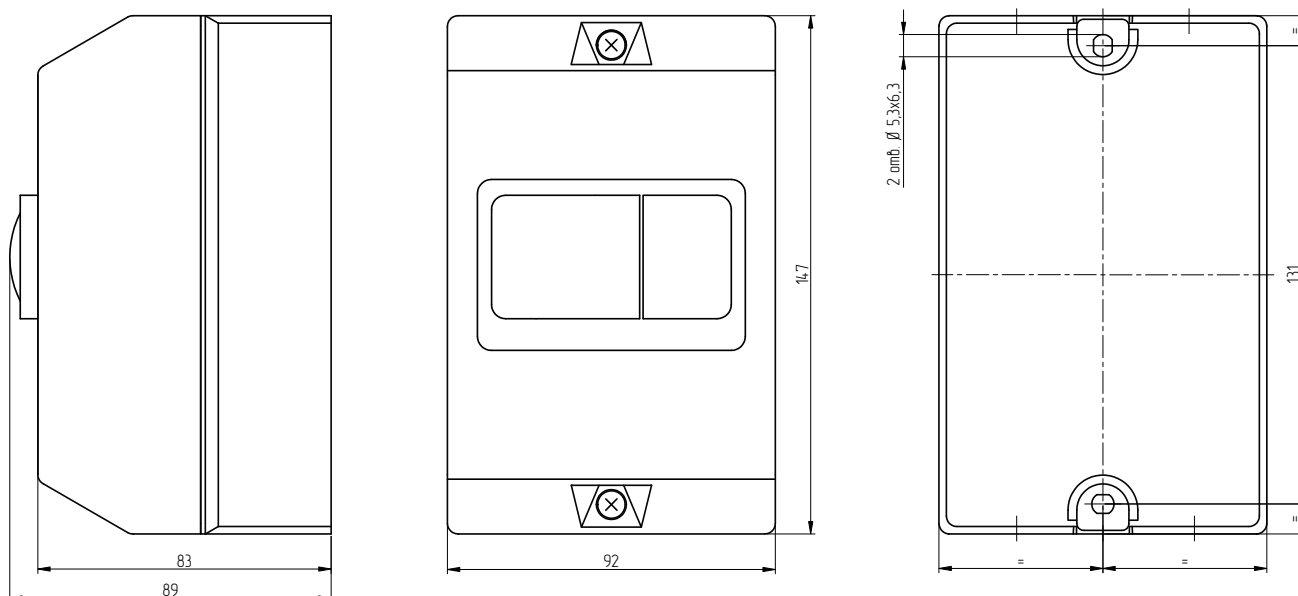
Защитный корпус для автоматических выключателей OptiStart ME GV2MC02
